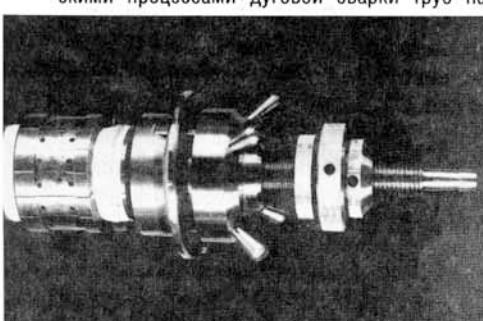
Внешний вид оснастки для сварки труб с фланцами
